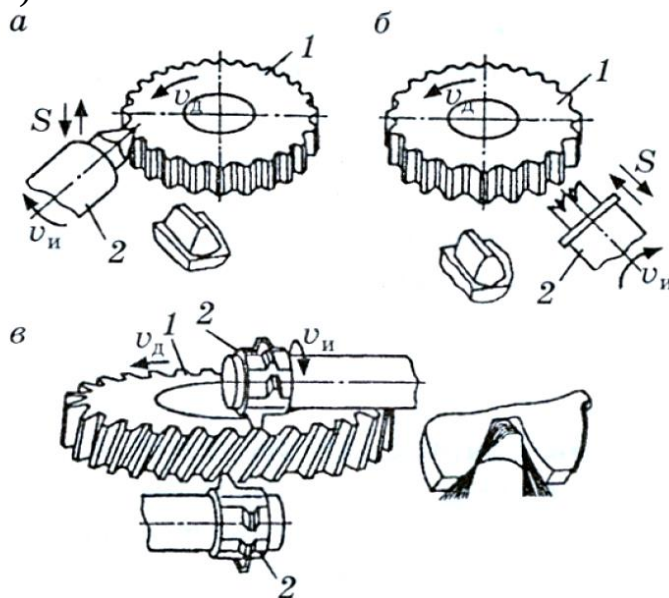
Способы закругления и снятия фасок на торцах зубьев различными фрезами: а – пальцевой; б – чашечной торцевой; в – дисковой фасонной; 1 – зубчатое колесо; 2 – инструмент
